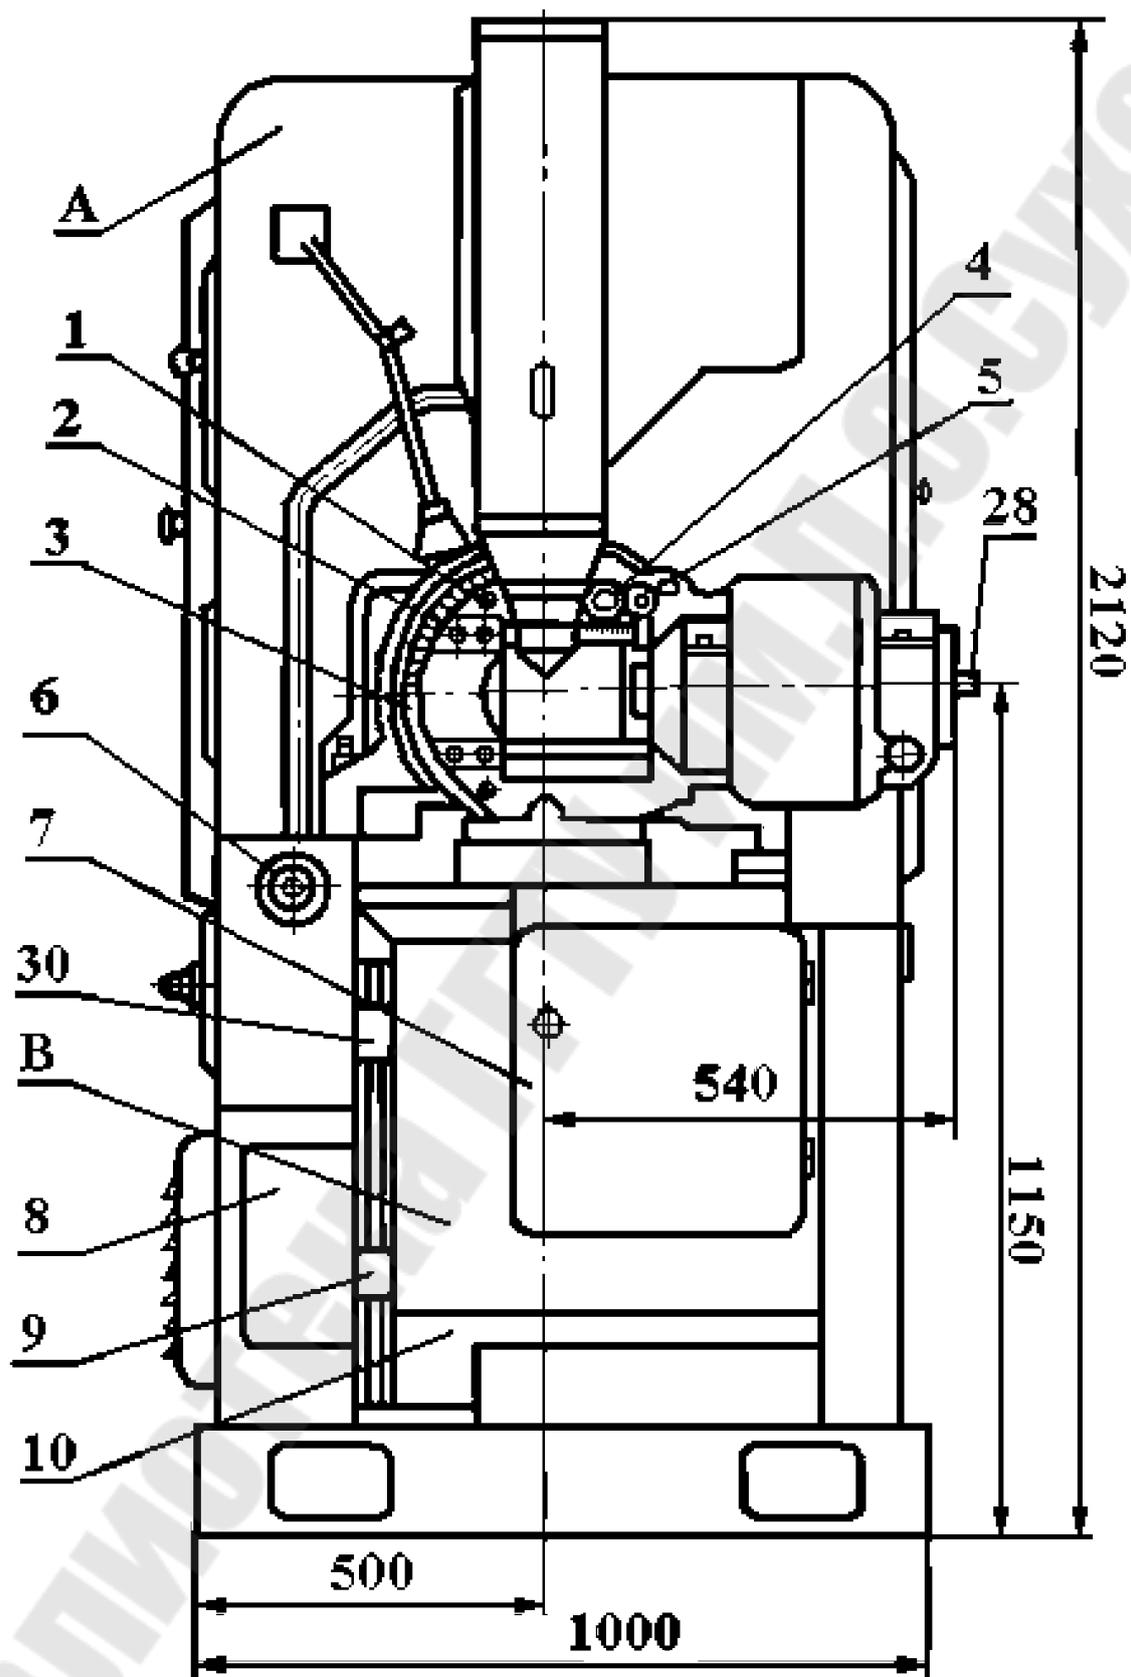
Общий вид зубофрезерного станка (вид спереди)
